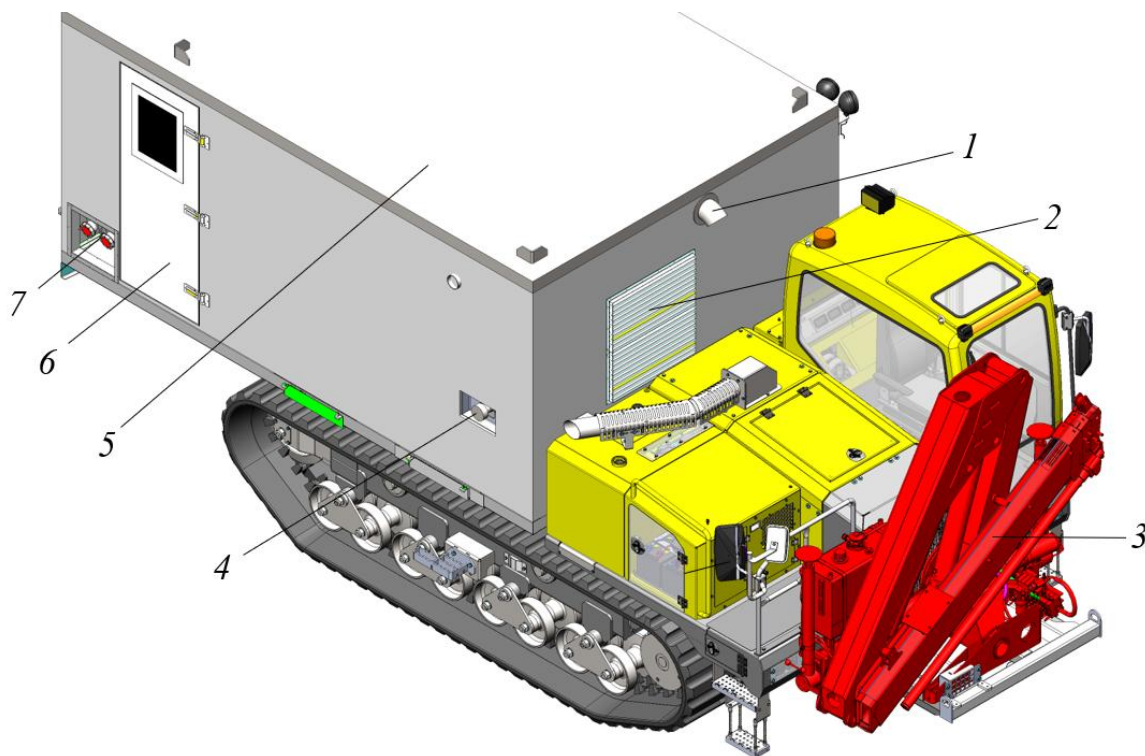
Агрегат гусеничный сварочный
